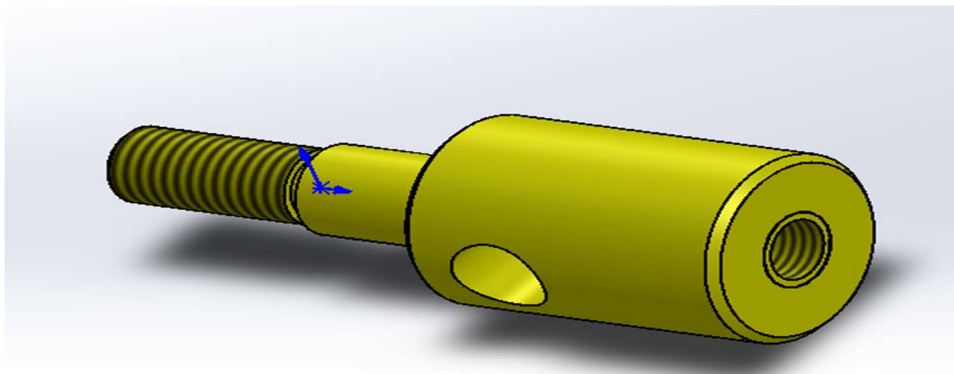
Vue 3D du supporte rotatif d'outil sous SolidWorks en 3D
